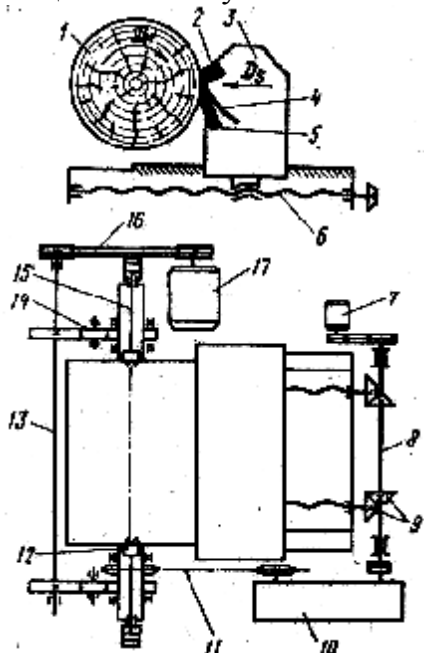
Принципиальная схема лущильного станка: 1 - чурак, 2 - прижимная линейка, 3 - суппорт, 4 - лента шпона, 5 - нож, 6 - винтовая передача, 7 - двигатель ускоренного отвода и подвода суппорта, 8, 13 - валы, 9 коническая передача, 10 - коробка передач, 11 - цепная передача, 12 - кулачок шпинделя, 14 - зубчатая передача, 15 - шпиндель, 16 - клиноремная передача, 17 - двигатель главного привода.
